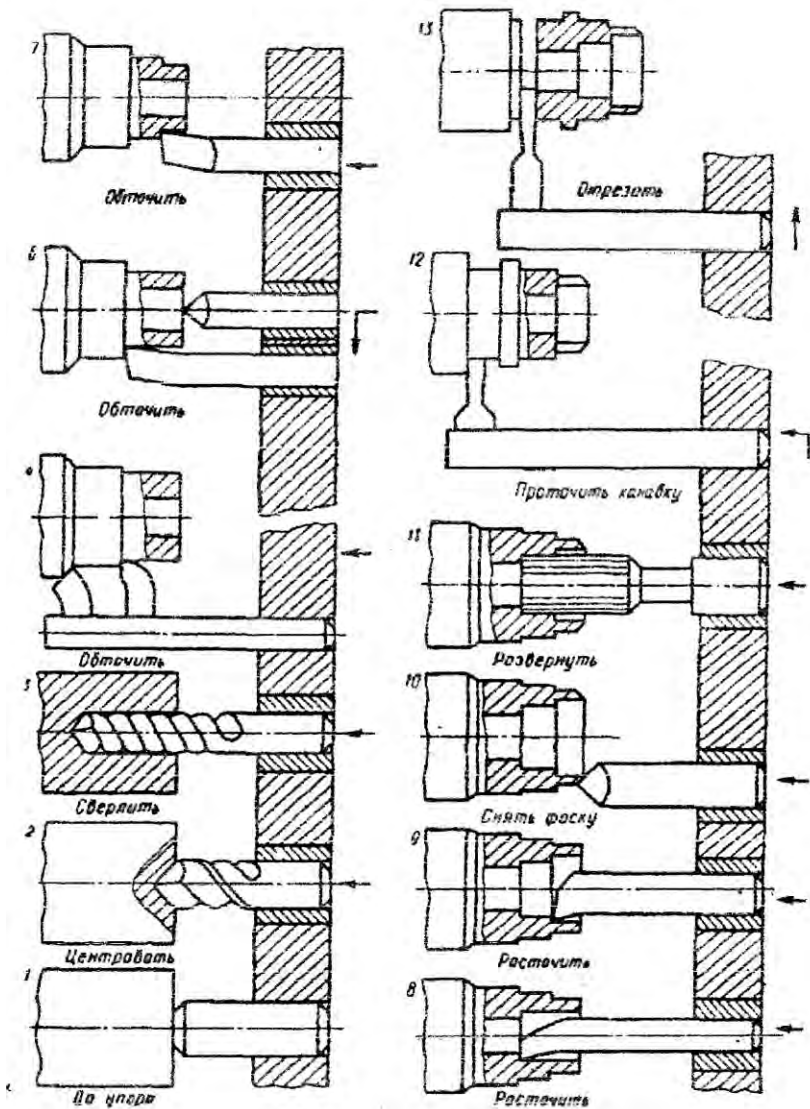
Схема обработки оправы на токарно-револьверном станке
